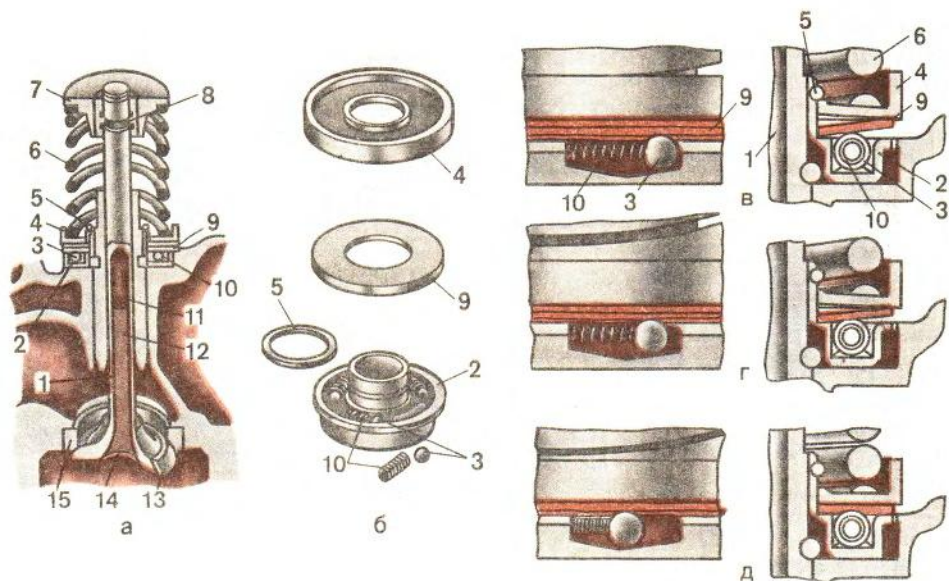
Выпускной клапан в сборе механизма газораспределения двигателя ЗИЛ-130 и схема поворота клапана:
